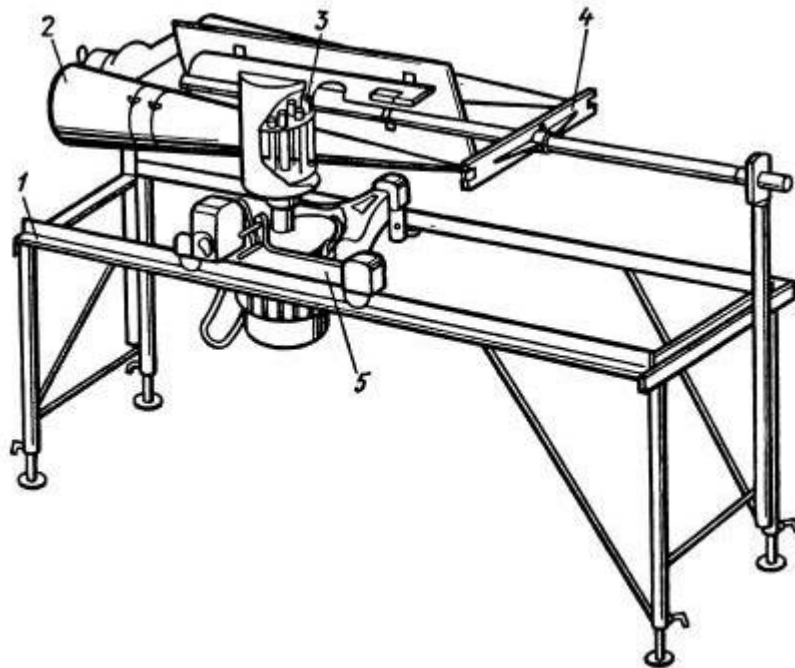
Станок СОШ-1 для обезжиривания шкурки: 1 – рама, 2 – болванка, 3 – фреза, 4 – крестовина, 5 – каретка.
